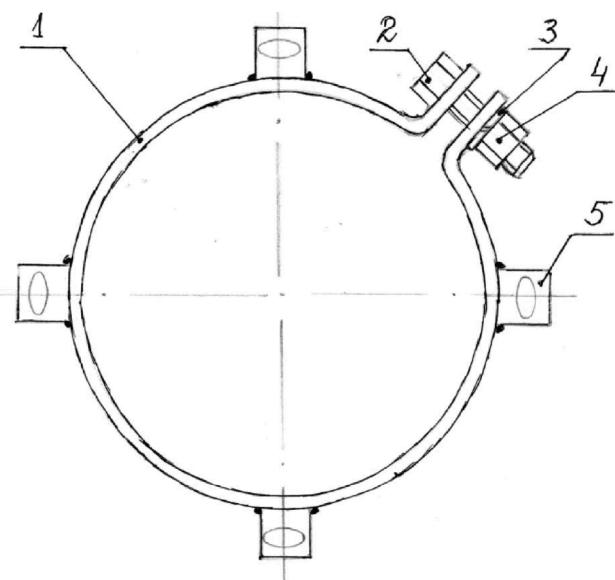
Конструкция для крепления средств защиты работающих на длинномерных высотных опорах (вид сверху)
